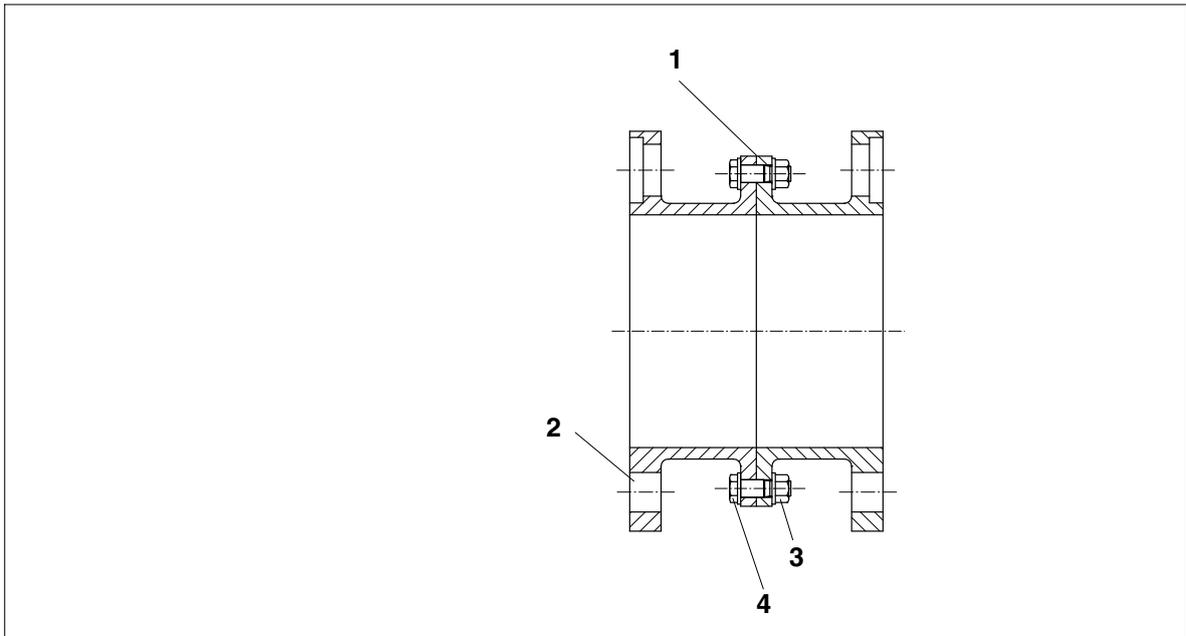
U-Hülse mit Passschrauben (ARC-8)
